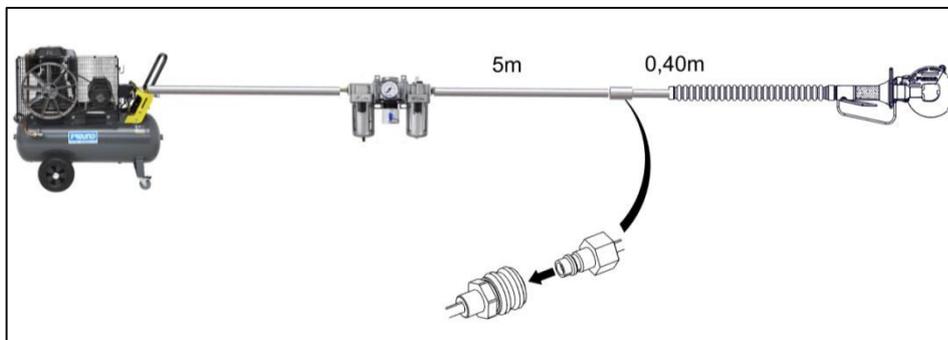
Schéma de raccordement pour la machine K16-P4\_evo2
